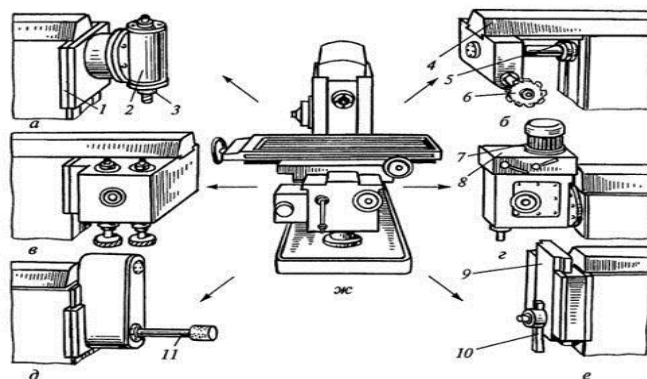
Приспособления, расширяющие технологические возможности фрезерных станков: а – дополнительная вертикально-фрезерная головка; б – приспособление для фрезерования реек; в – двухшпиндельная фрезерная головка; г – сверлильная головка; д – шлифовальная головка; е – долбежная головка; ж – общий вид станка; 1 – устройство для крепления на станке; 2 – инструментальная головка; 3 – концевая фреза; 4 – хобот станка; 5 – шпиндель станка; 6 – фреза; 7 – приводной электродвигатель; 8 – корпус головки; 9 – салазка инструмента; 10 – инструментальная оправка; 11 – шпиндель шлифовальной головки
